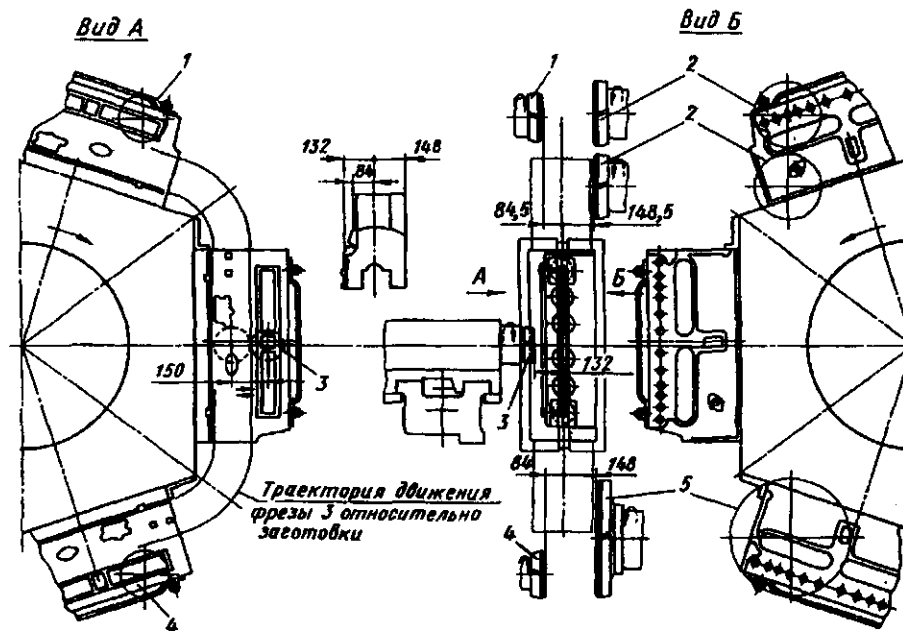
Схема фрезерования плоских поверхностей блока на карусельном барабанно-фрезерном станке
